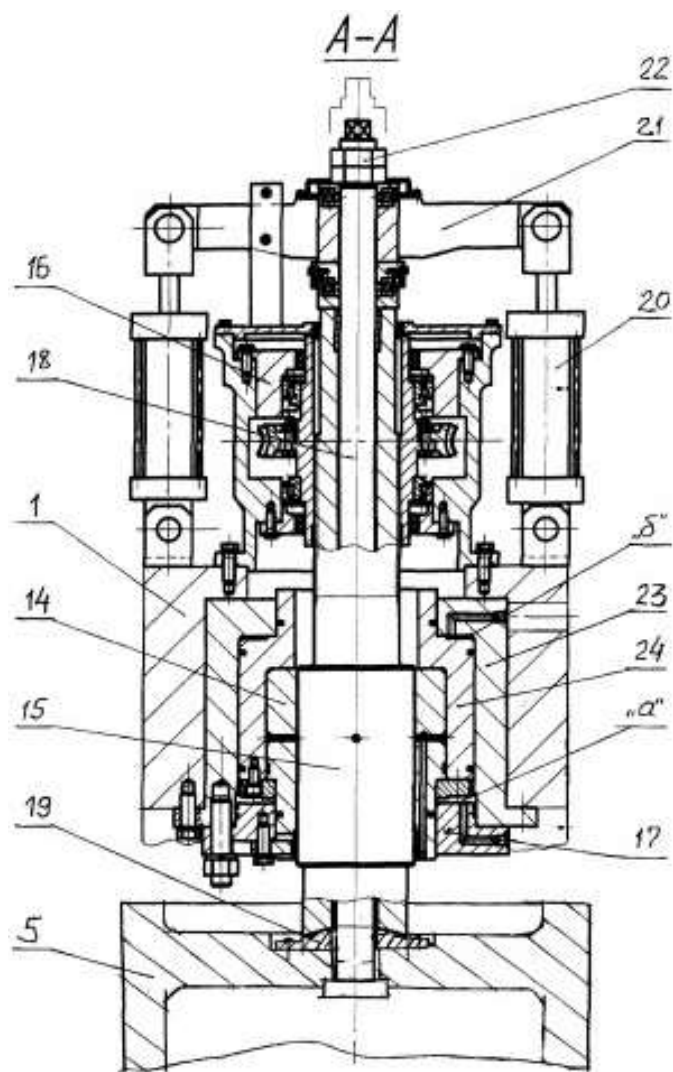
Рабочая клетка стана поперечно винтовой прокатки. Вид сбоку
